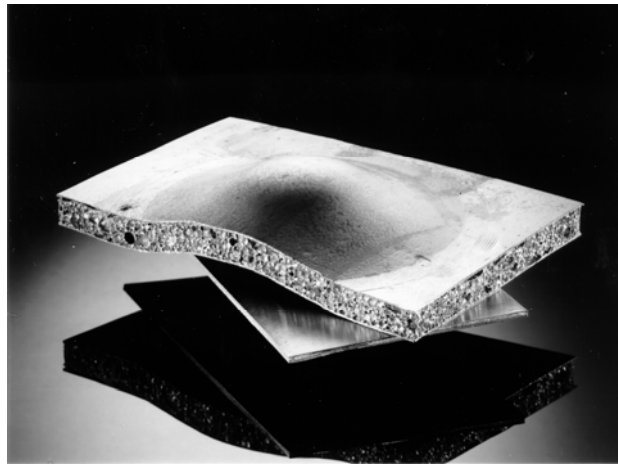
Sandwichstruktur aus Aluminiumschaum und Stahldeckblechen
